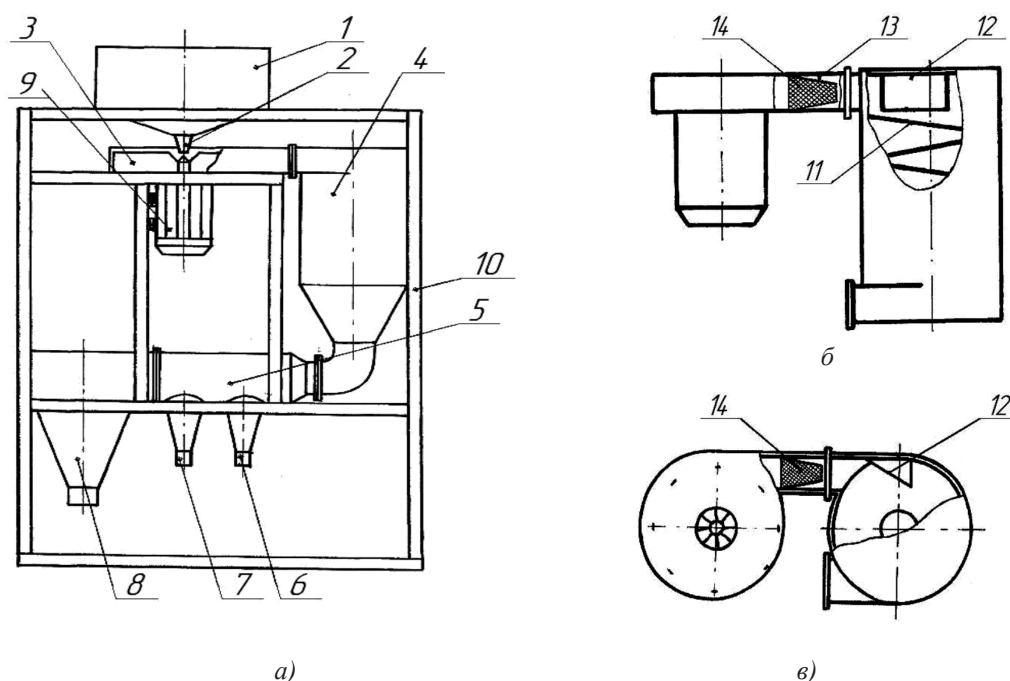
Устройство для шелушения зерна: а) – общий вид устройства; б) – вентилятор с шелушильной камерой (вид сбоку); в) – вентилятор с шелушильной камерой (вид сверху); 1 – питающий бункер; 2 – загрузочный патрубок; 3 – лопатки вентилятора; 4 – шелушильная камера; 5 – пневмосепаратор; 6, 7 – отводы готовой продукции; 8 – центробежный осадитель; 9 – электродвигатель; 10 – станина; 11 – винтообразная рабочая поверхность; 12 – рабочая пластина; 13 – нагнетательный патрубок; 14 – сетчатый рабочий орган
